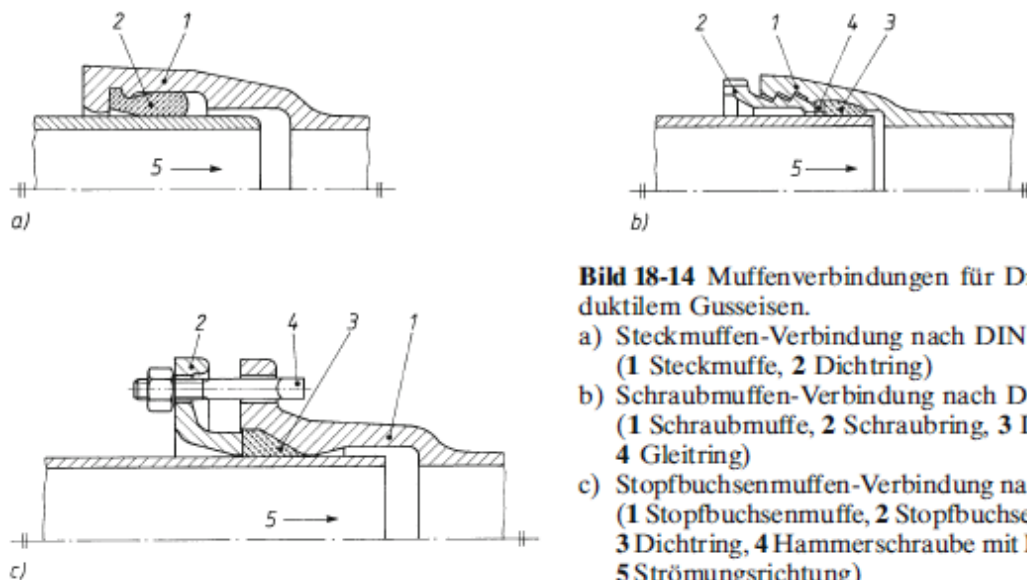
Muffenverbindungen für Druckrohre aus duktilem Gusseisen.
